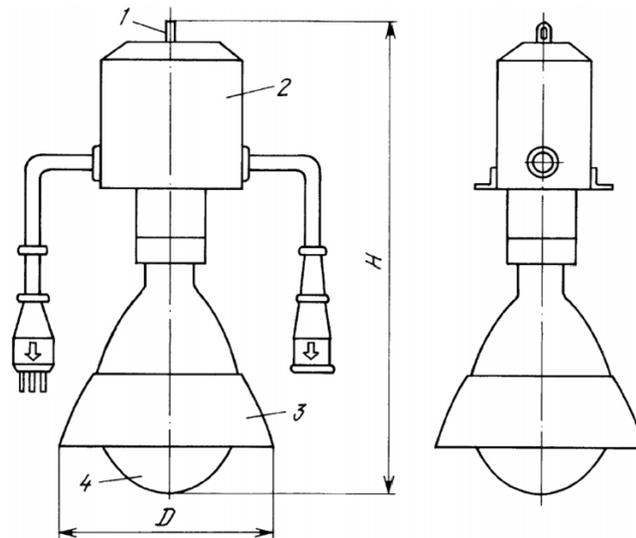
Габаритные размеры светильника с лампой типа ДРЛФ 400-2:
